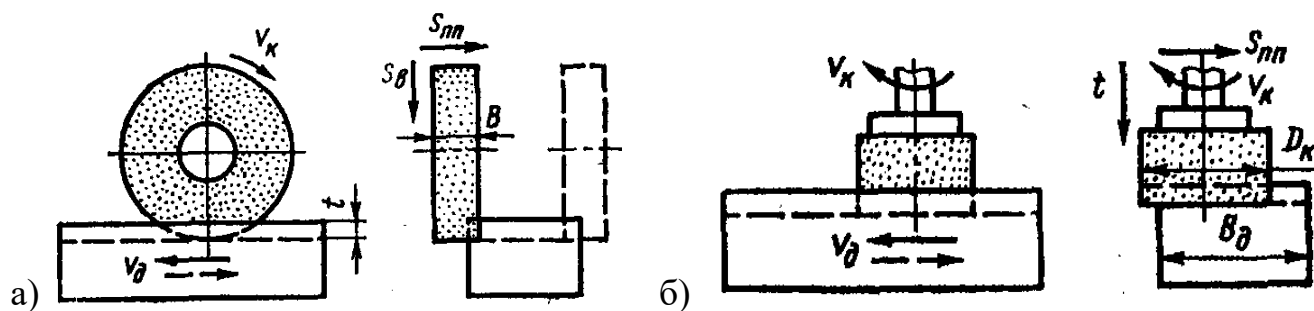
Схемы плоского шлифования на станке с прямоугольным столом: а – периферией круга, б – торцом круга
